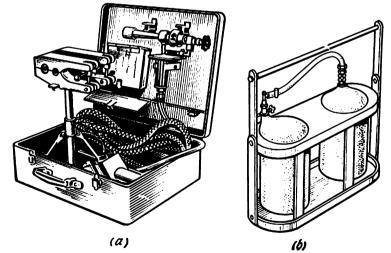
Lot d'outils et de dispositifs pour le soudage au propane-butane:
